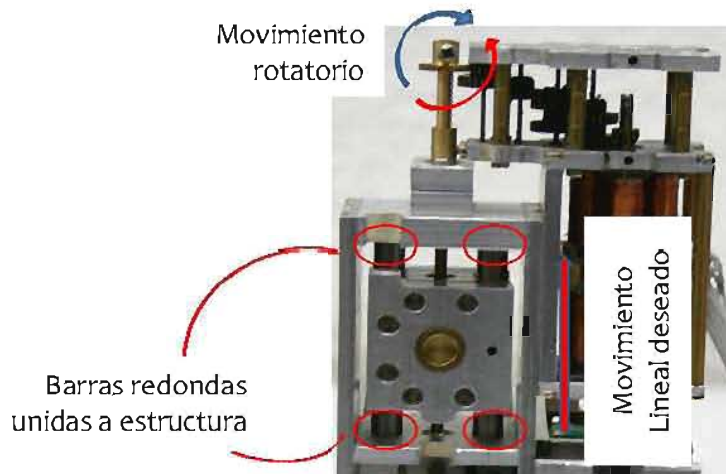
Barras redondas fijas a estructura de la máquina [6]
